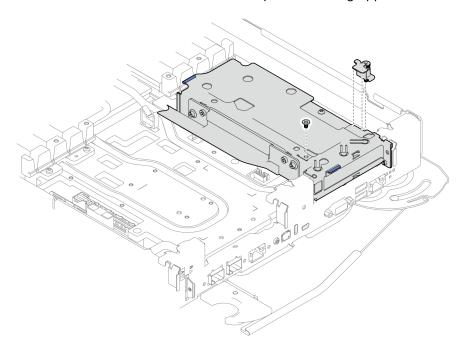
Entfernen der Klemme und Schraube der Adapterkartenbaugruppe
